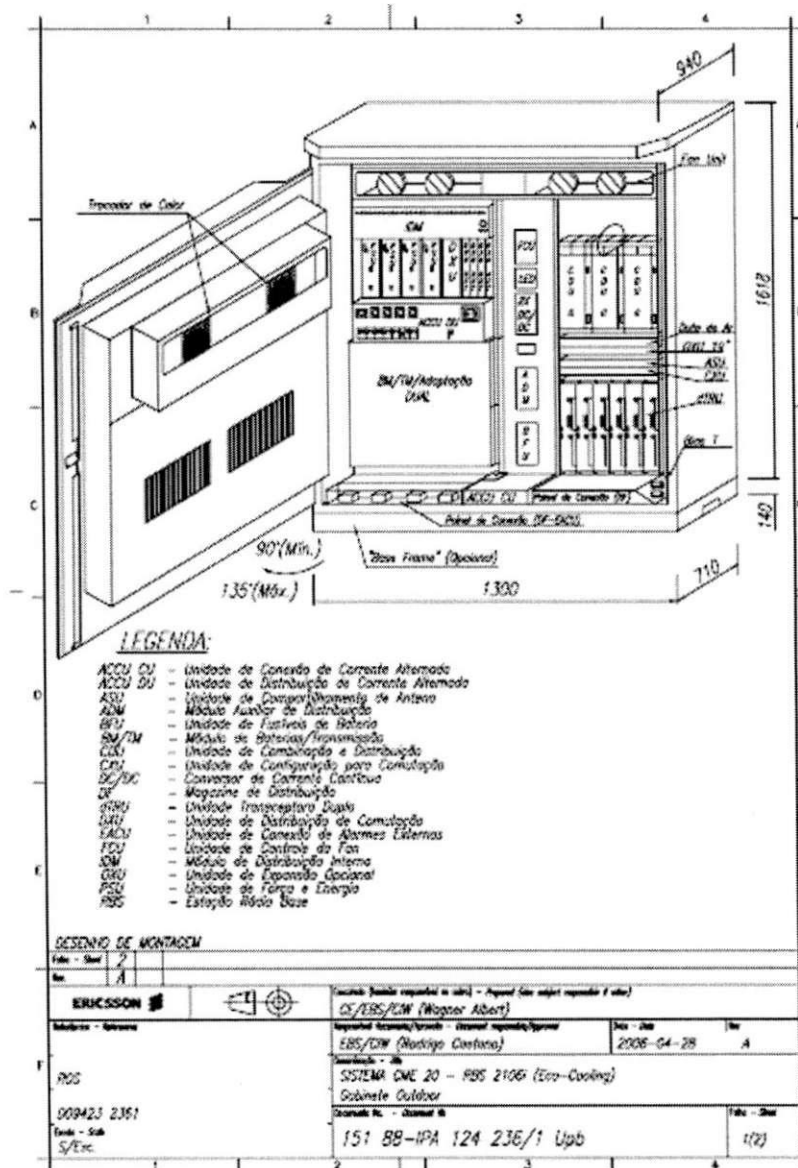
Plano de face da BTS GSM 2106 Dual Band
